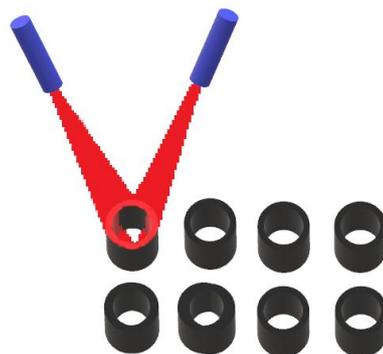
Variante 3- Simultanschweißen
